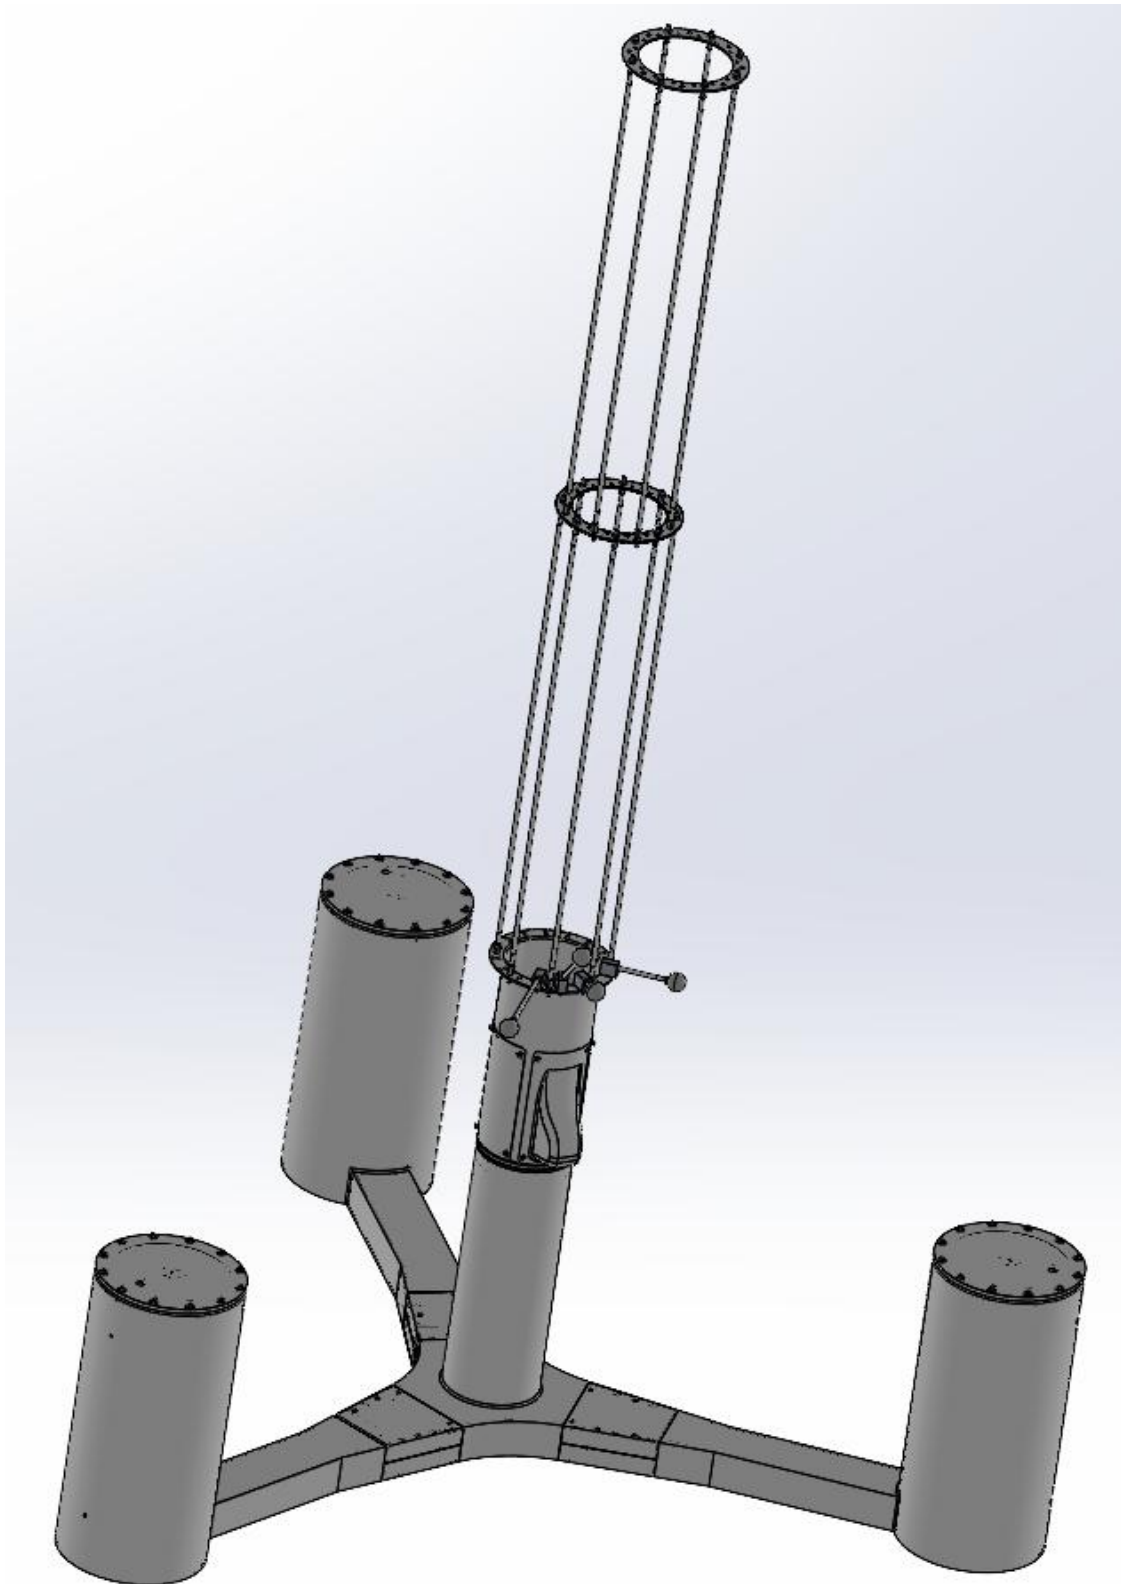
Vue CAO du modèle complet (plateforme et superstructure)
